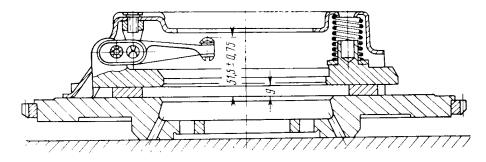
Установка на маховик нажимного диска с кожухом для регулировки рычагов
